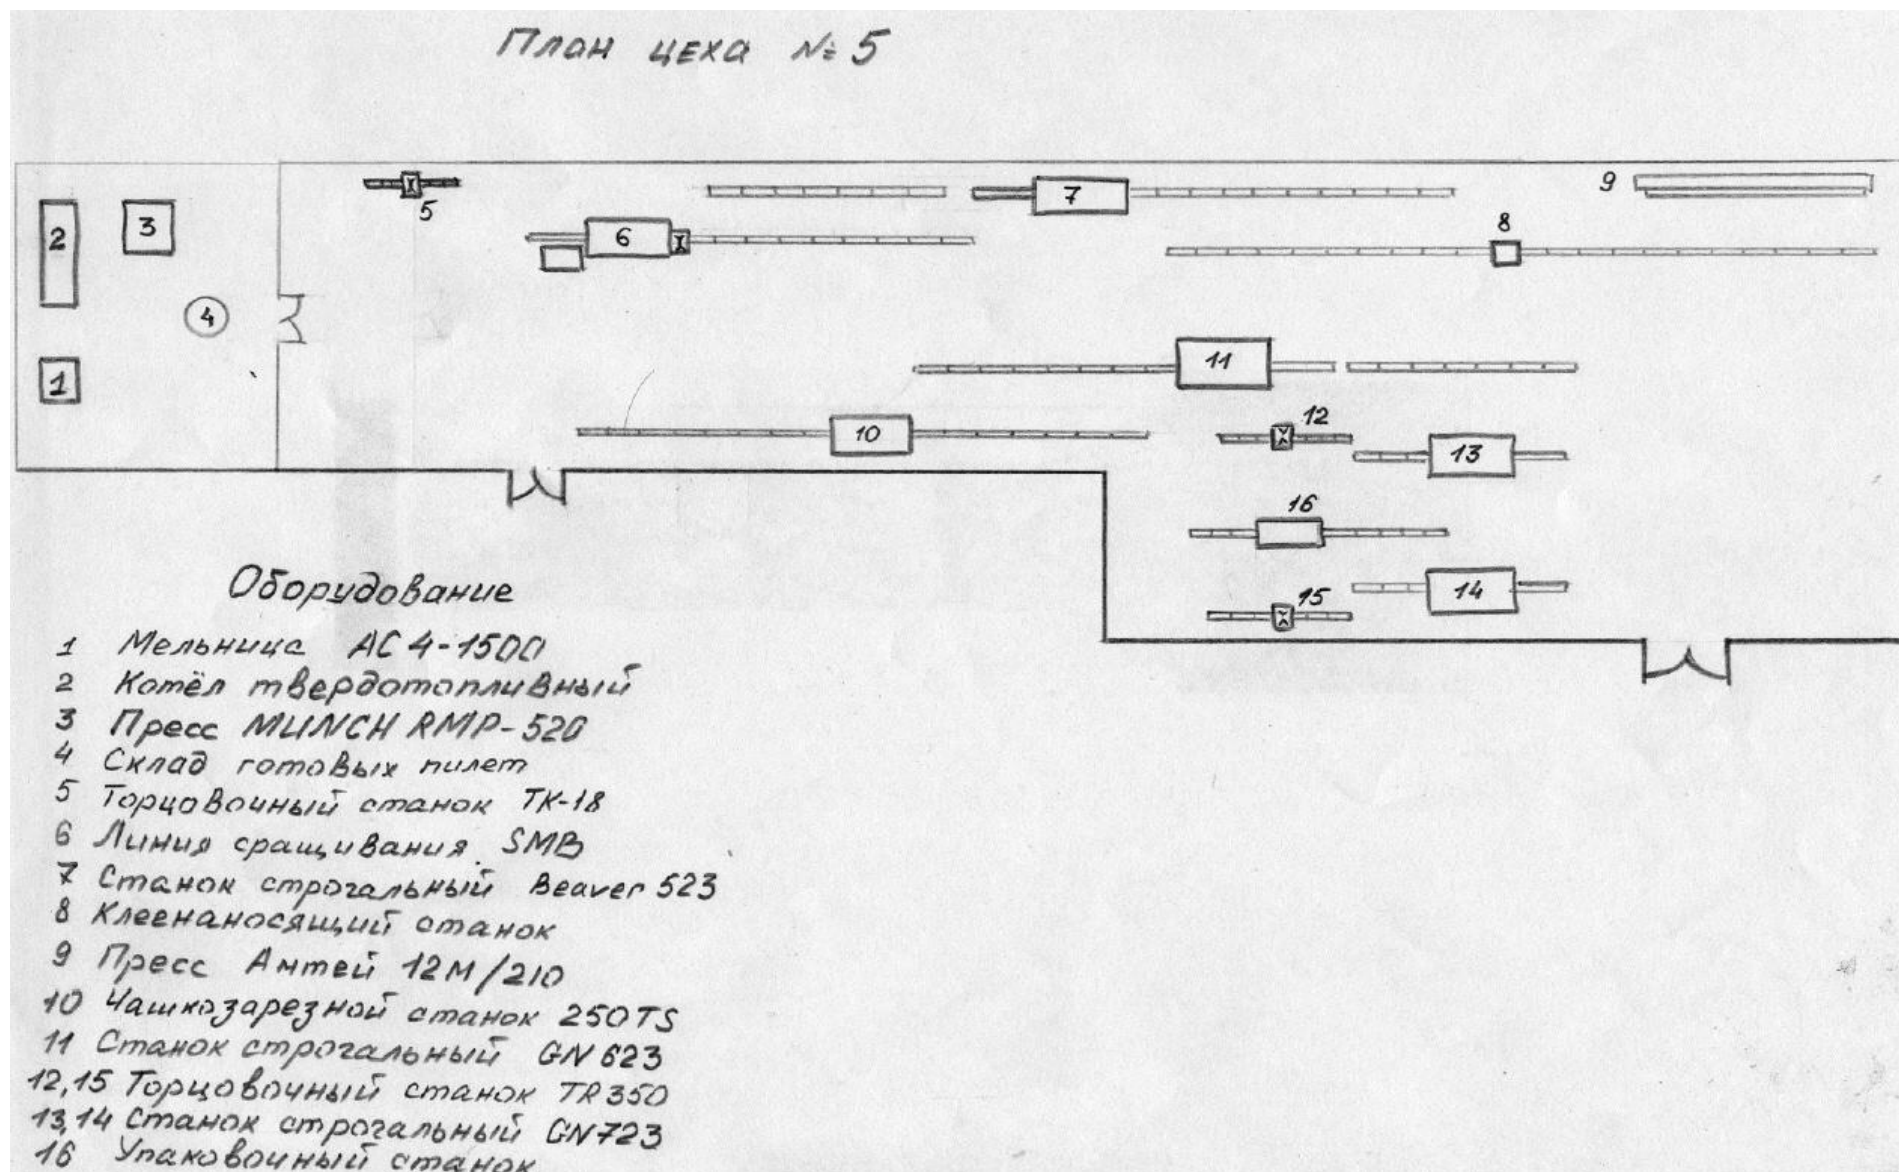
План размещения оборудования в цехе окончательной деревообработки
